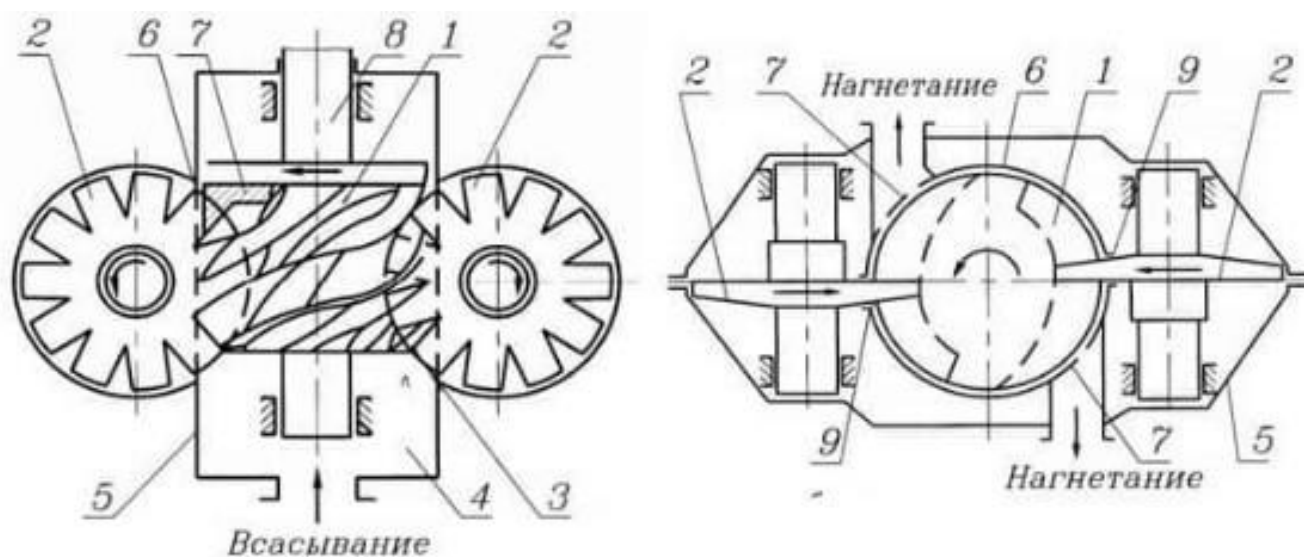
Полугерметичный винтовой маслозаполненный компрессор в разрезе.
